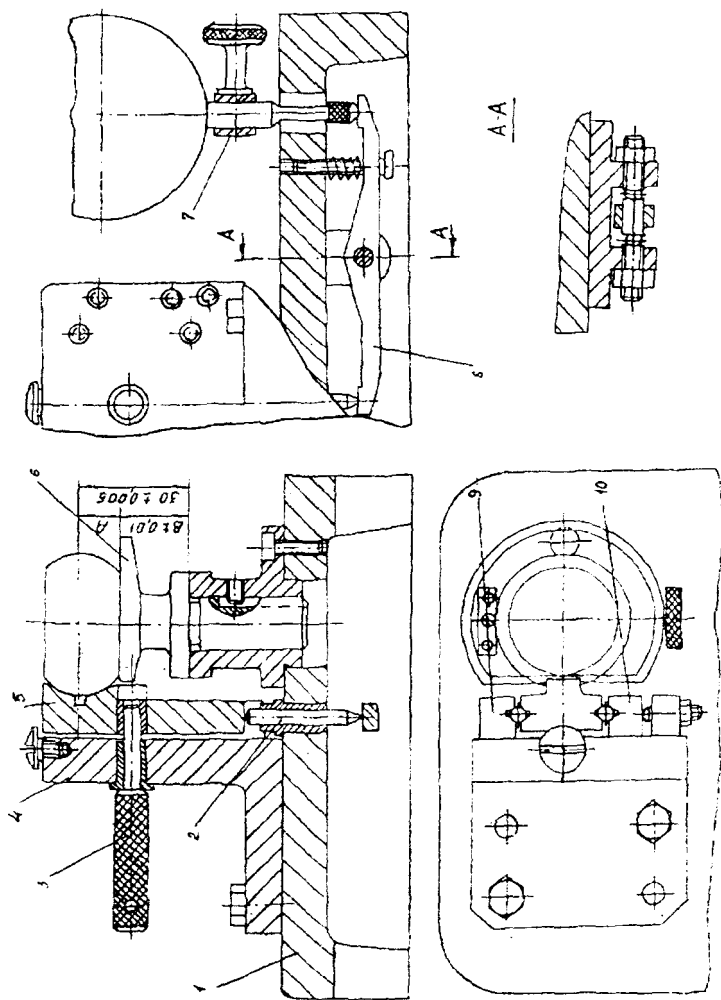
Приспособление для контроля смещения сферы относительно торцов
